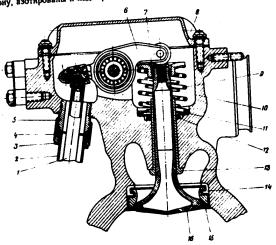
Рычаг клапана, собранный в цилиндре (вид сверху).
